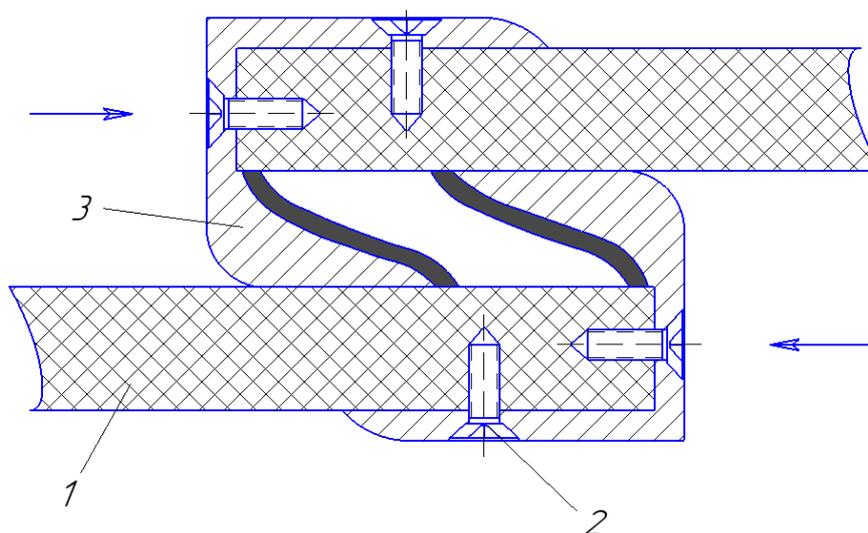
Схема шипового сцепления конечных частей раздвижных дверей:
